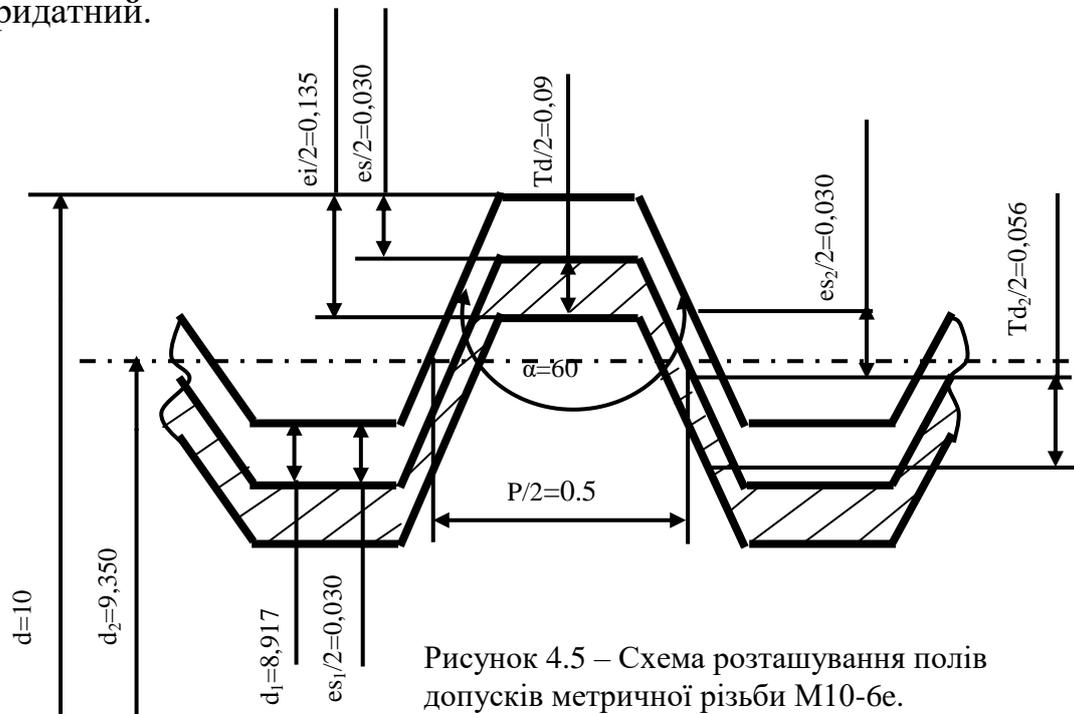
Схема розташування полів допусків метричної різьби М10-6е.
